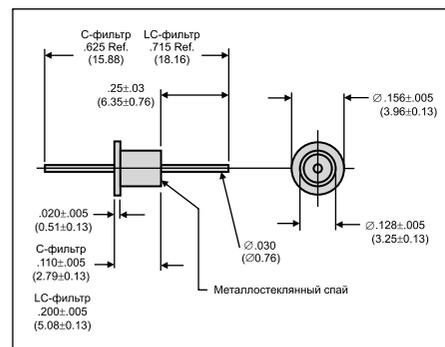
Чертеж корпуса серий SCI-9900 и SCI-9980
